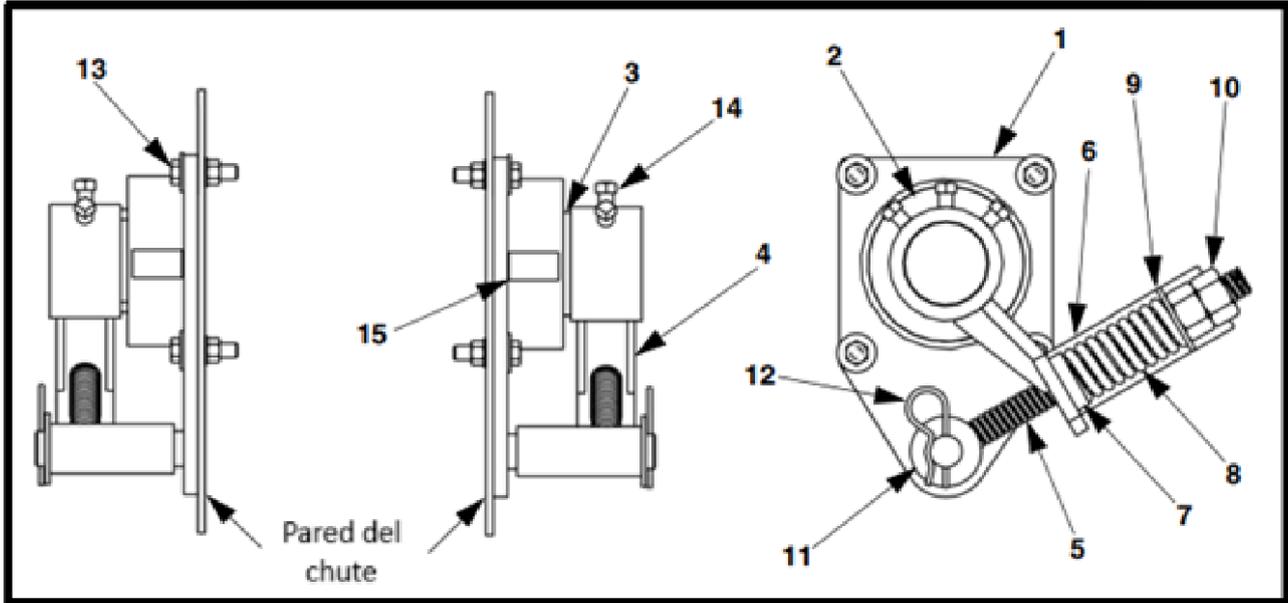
Ensamble del tensionador mecánico doble Martin ® XHD: P/N 38003-2.
